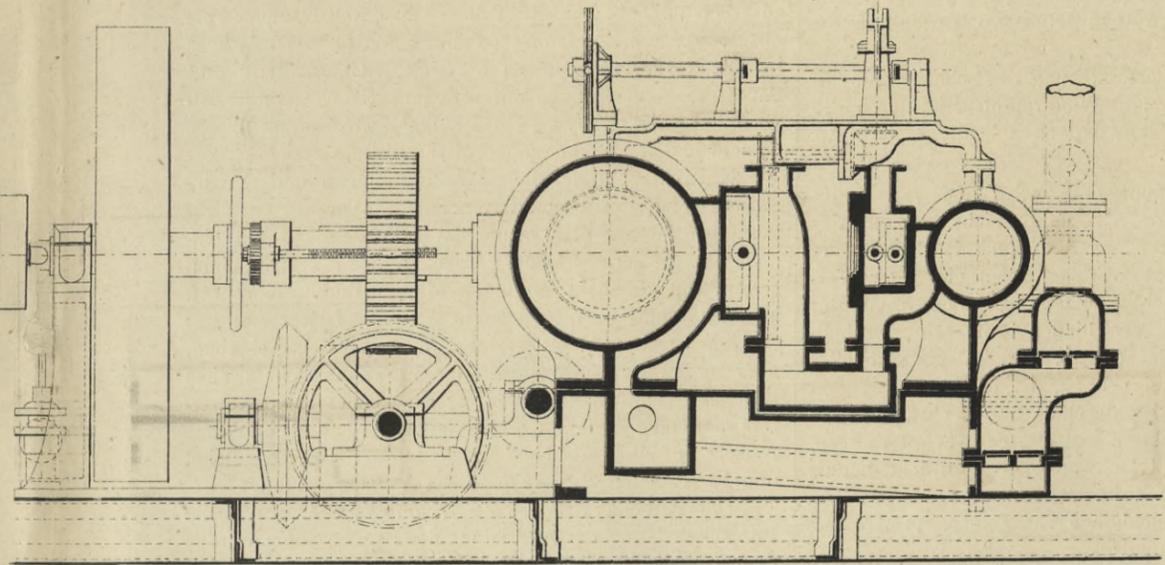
Querschnitt durch Kondensator und Luftpumpe.
